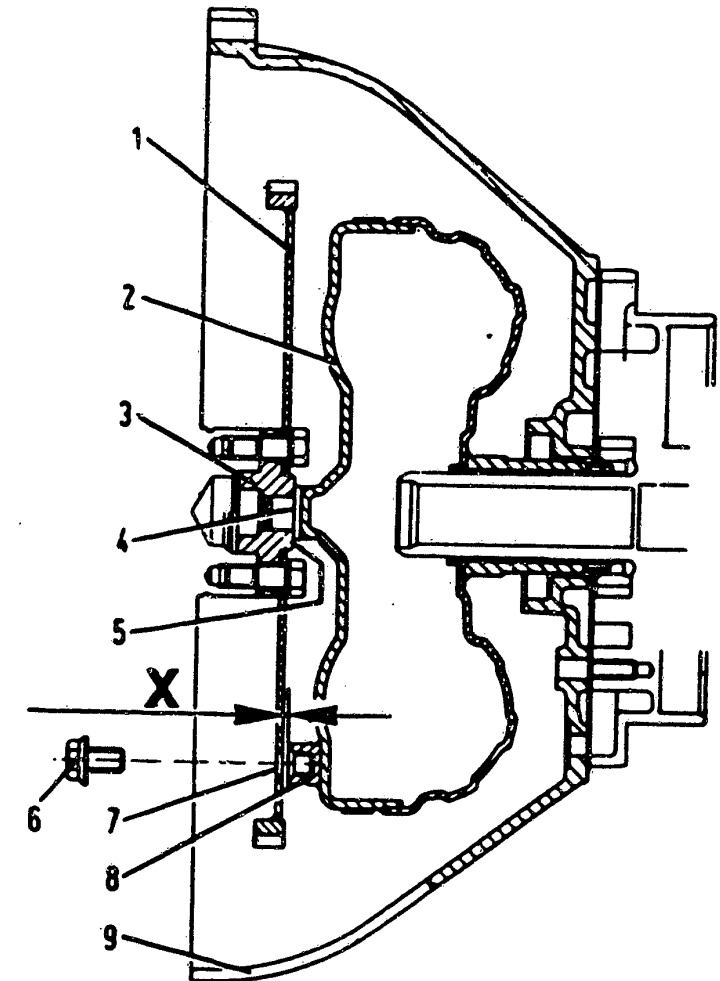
Der Abstand $X = 0,20 \dots 1,21 \text{ mm}$ muss kontrolliert werden, bevor der Wandler an das Schwungrad geschraubt wird. 1 Schwungrad – 2 Wandler – 3 Befestigungsflansch – 4/5 Kontaktflächen – 6/7 Befestigungsschraube und -bohrung – 8 Befestigungsklötze – 9 vorderes Getriebegehäuse.
